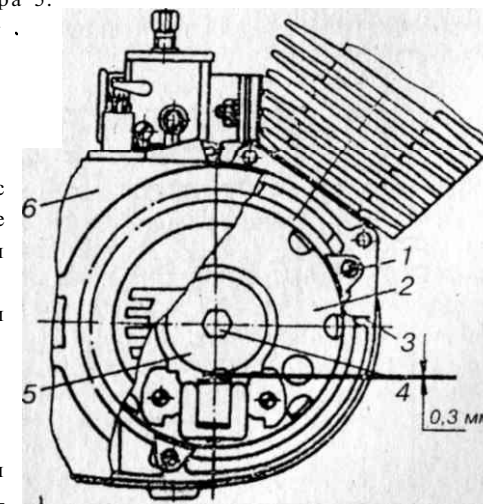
Порядок установки зажигания: 1 - винт крепления статора; 2 - статор; 3 - риска на картере; 4 - болт крепления ротора; 5 - ротор; 6 - правая крышка картера
